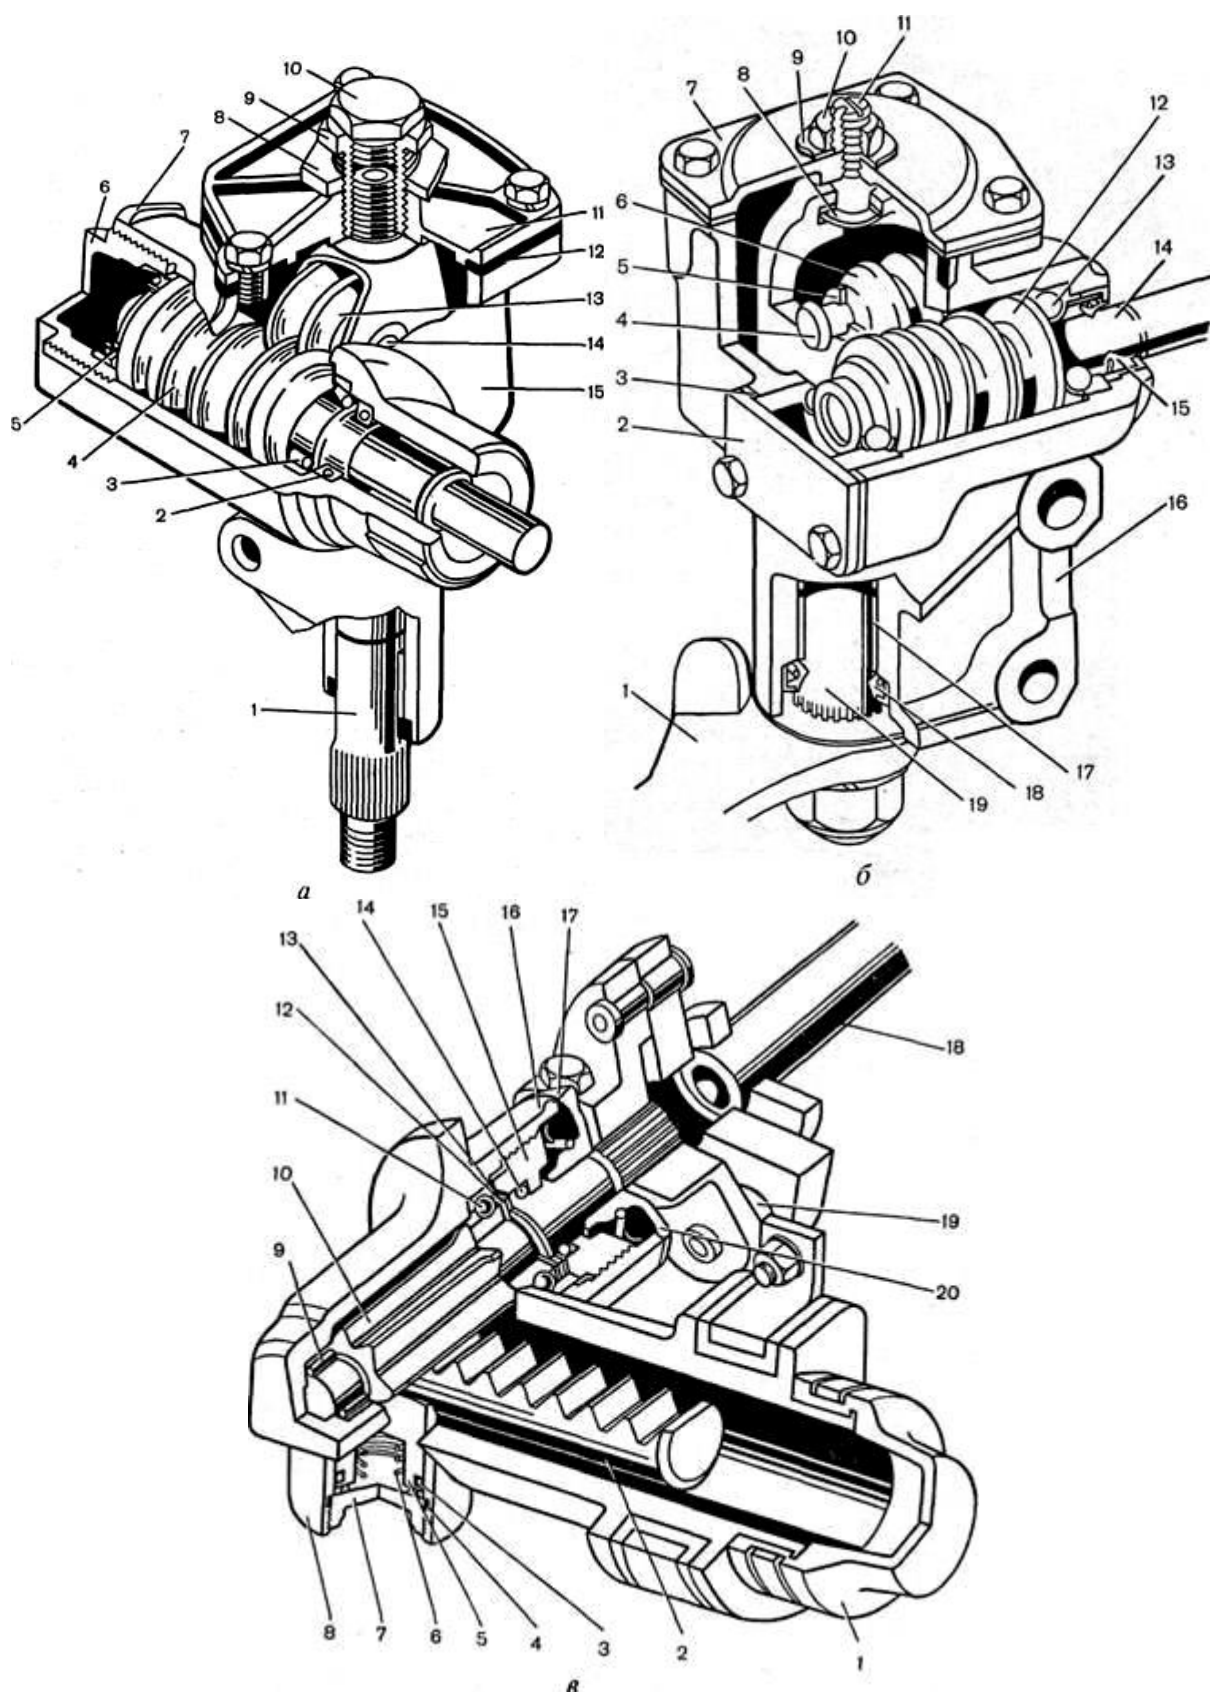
Рулевые механизмы: *а* — автомобиля ИЖ-2715: 1 — вал сошки; 2 — манжета; 3, 5 — подшипники червяка; 4 — глобоидальный червяк; 6 — регулировочная гайка подшипника червяка; 7, 8 — стопорные гайки; 9 — резьбовая втулка вала сошки; 10 — пробка наливного отверстия; 11 — крышка картера; 12 — прокладка; 13 — двухгребневый ролик; 14 — ось ролика; 15 — картер рулевого механизма; *б* — автомобиля ВАЗ-2121: 1 — рулевая сошка; 2 — крышка нижняя; 3 — регулировочные
